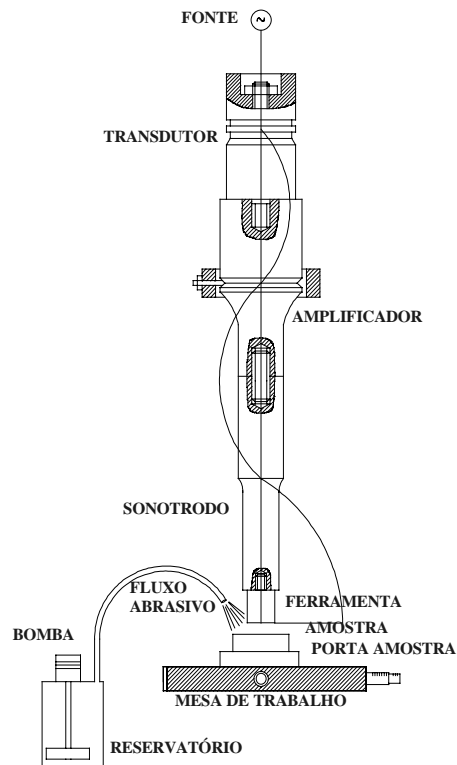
Equipamento de usinagem por abrasão ultra-sonora.
